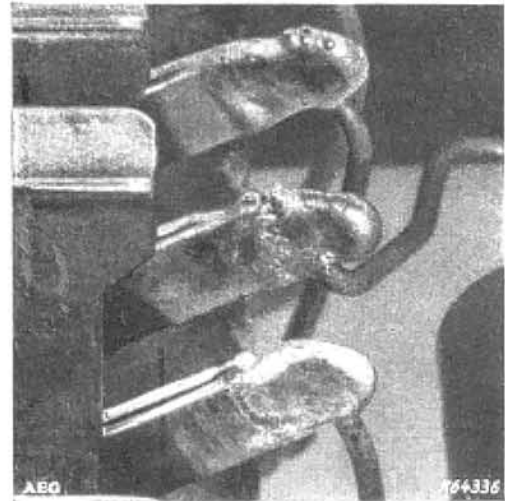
Gut ausgeführte Schweißung von Kupferdraht zwischen 2 Bronzefedern.
